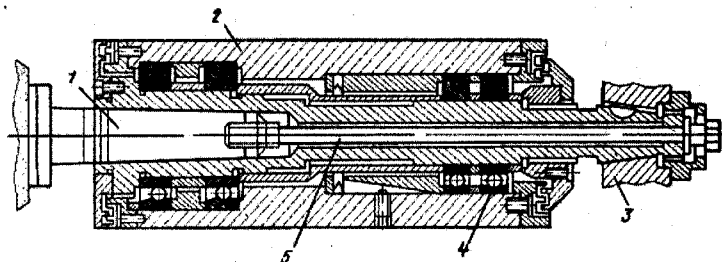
Шлифовальная головка универсально-заточного станка
